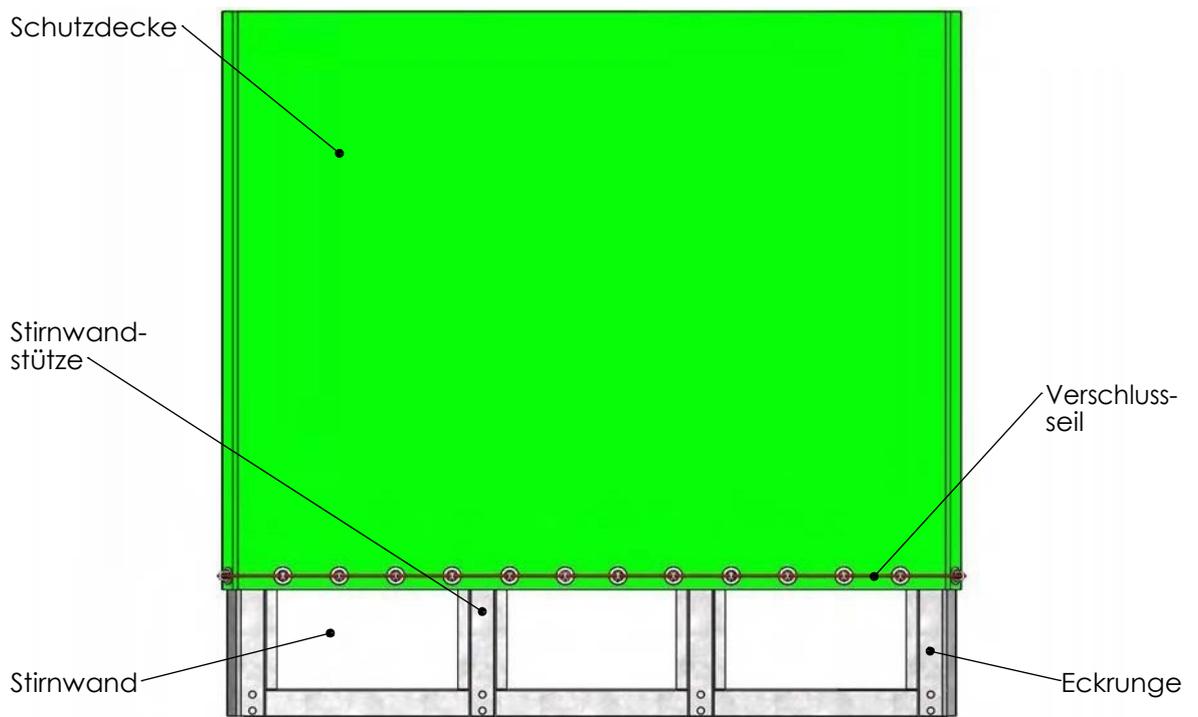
Stirnwand: Schutzdecke ohne Ausschnitt
